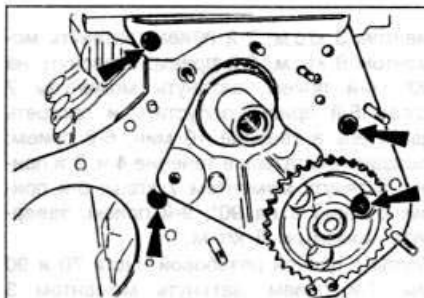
Стрелками показаны болты крепления проставки крышки привода распределительного вала
